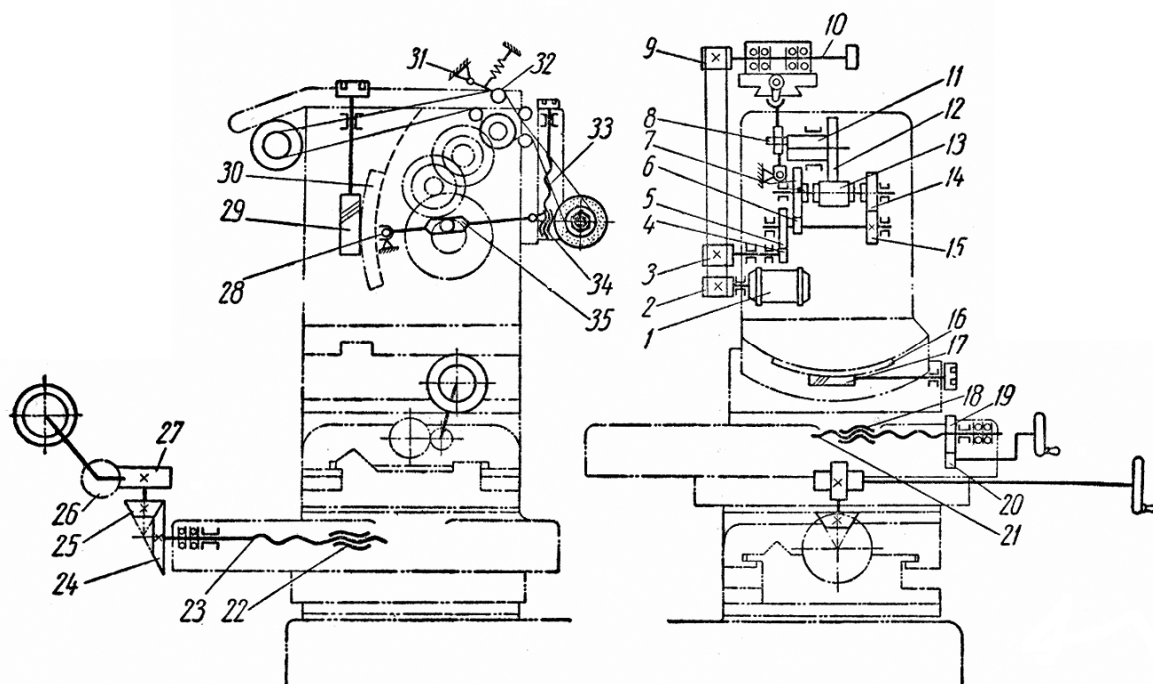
Кинематическая схема шлифовальной головки станка мод. 395М1:
